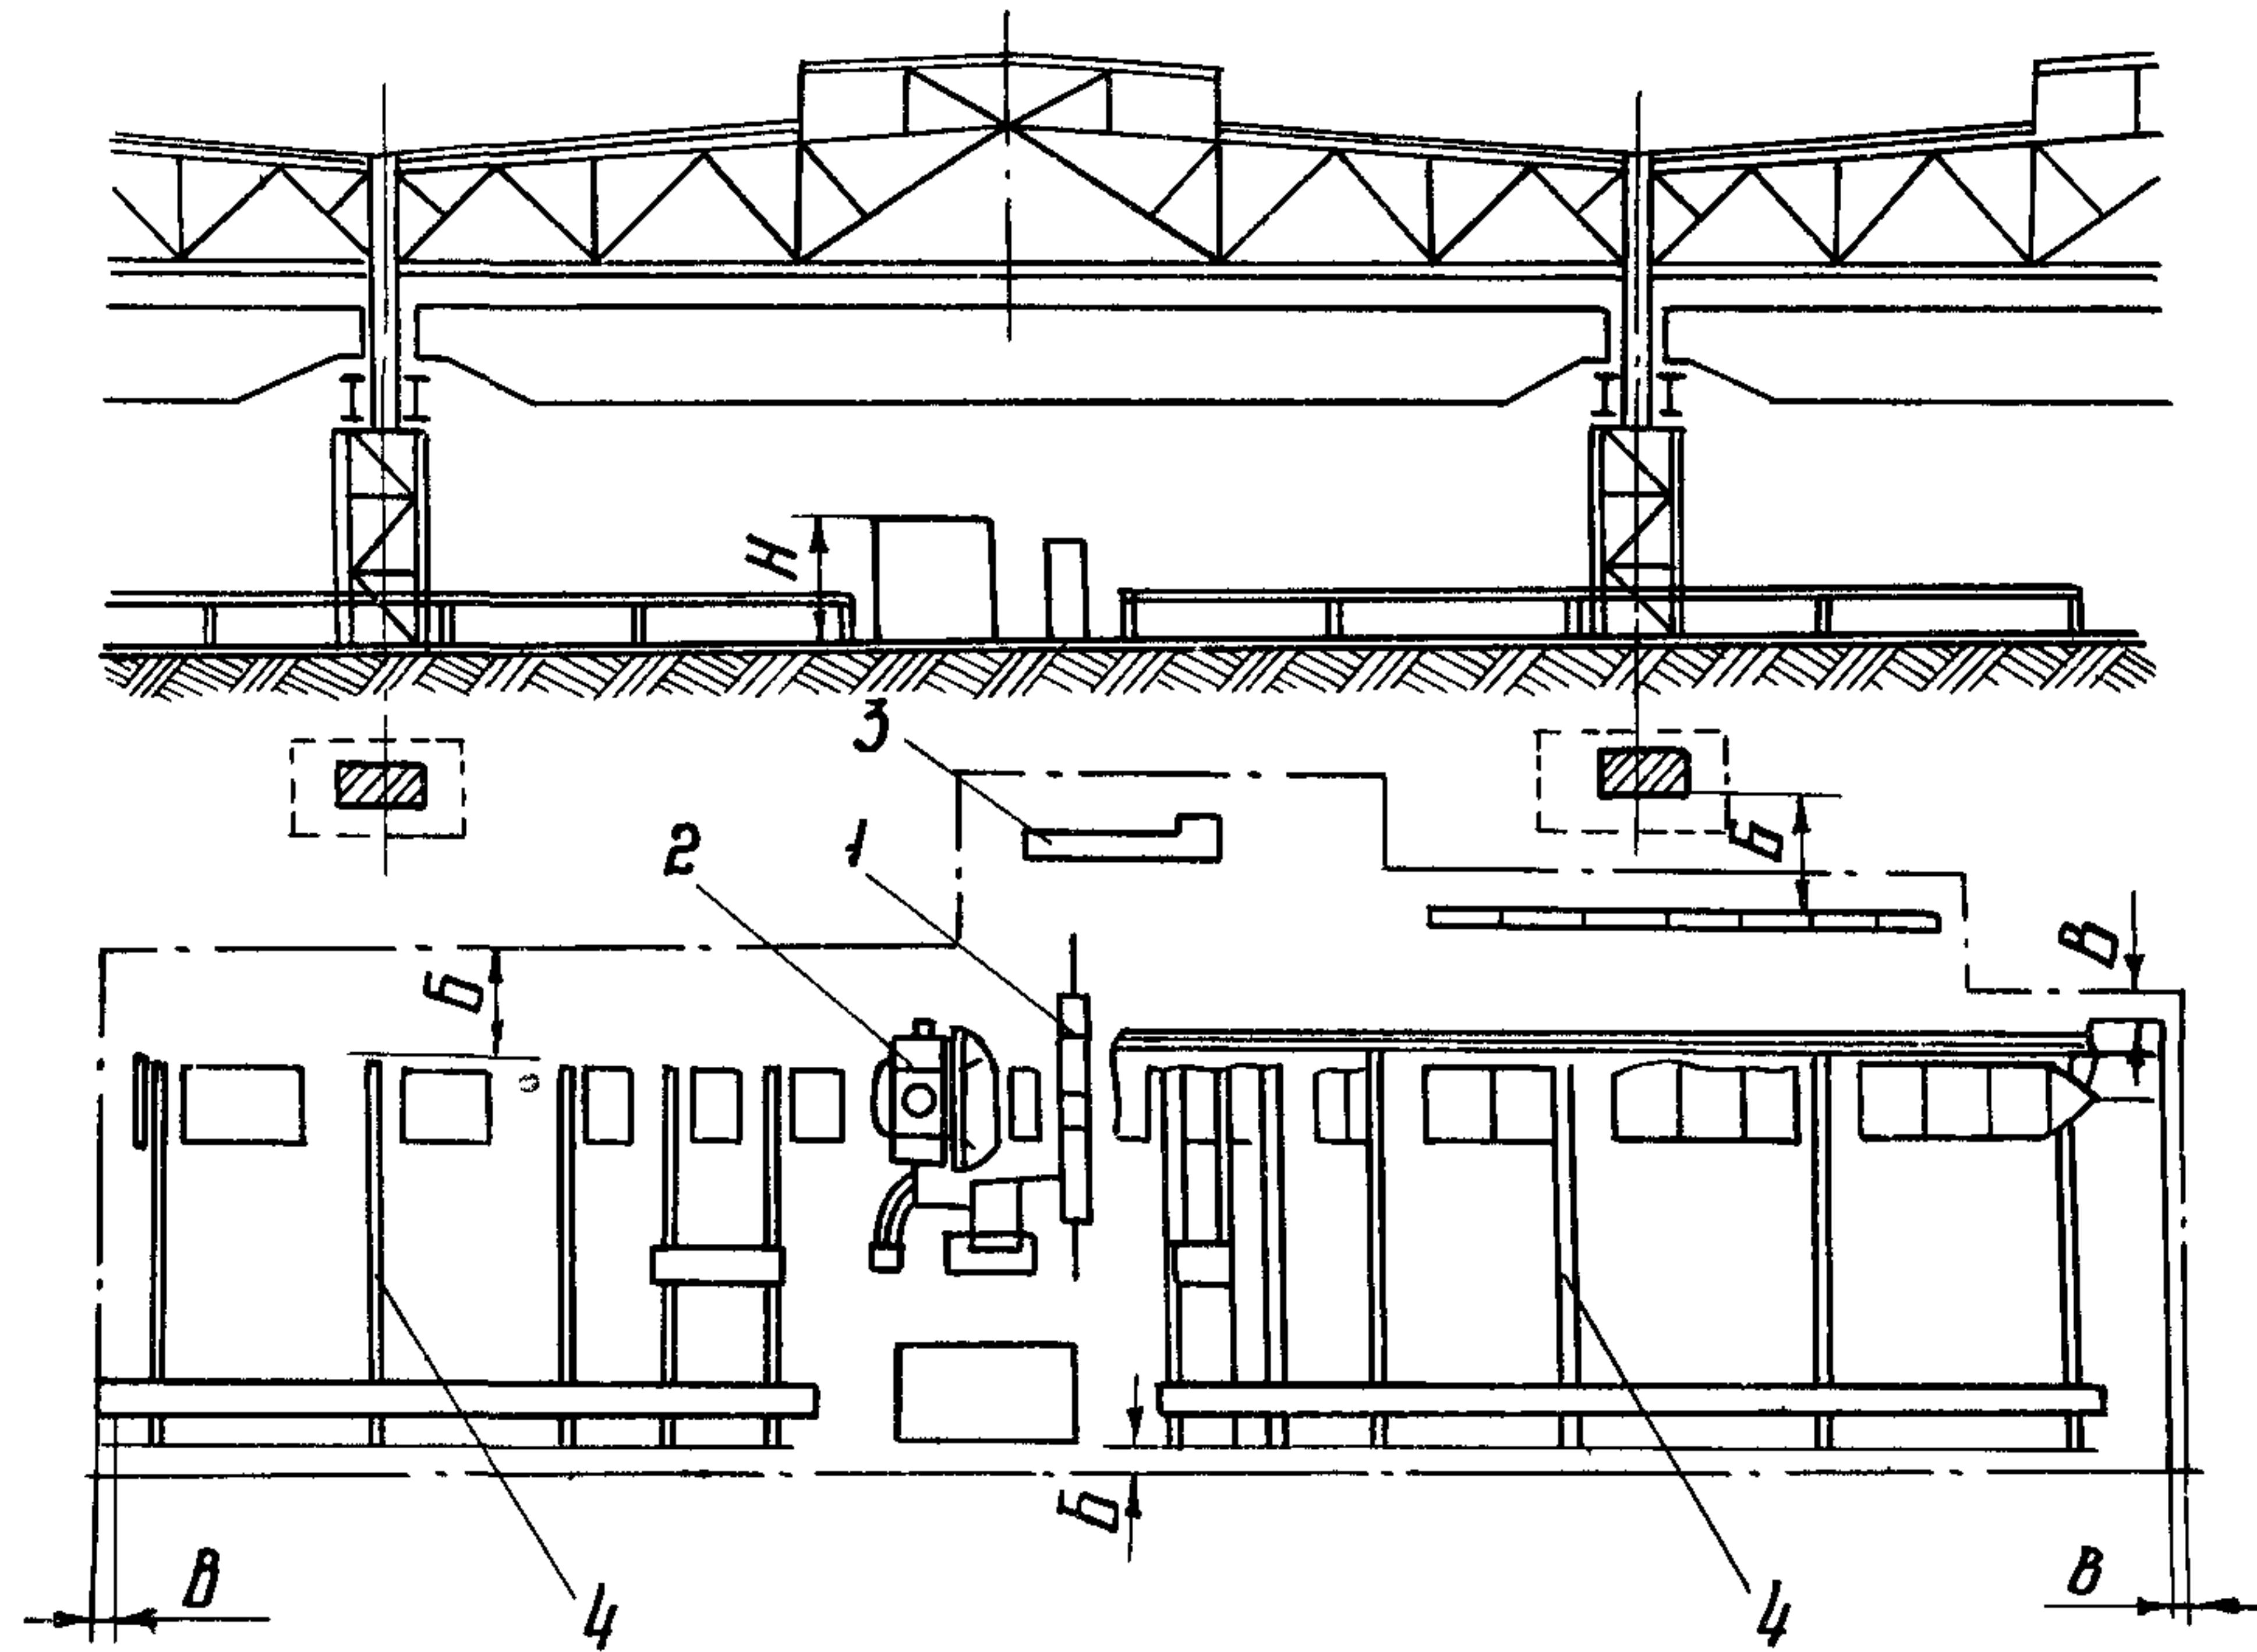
Размещение поточной линии для резки и сверления отверстий фирмы "Вагнер":
